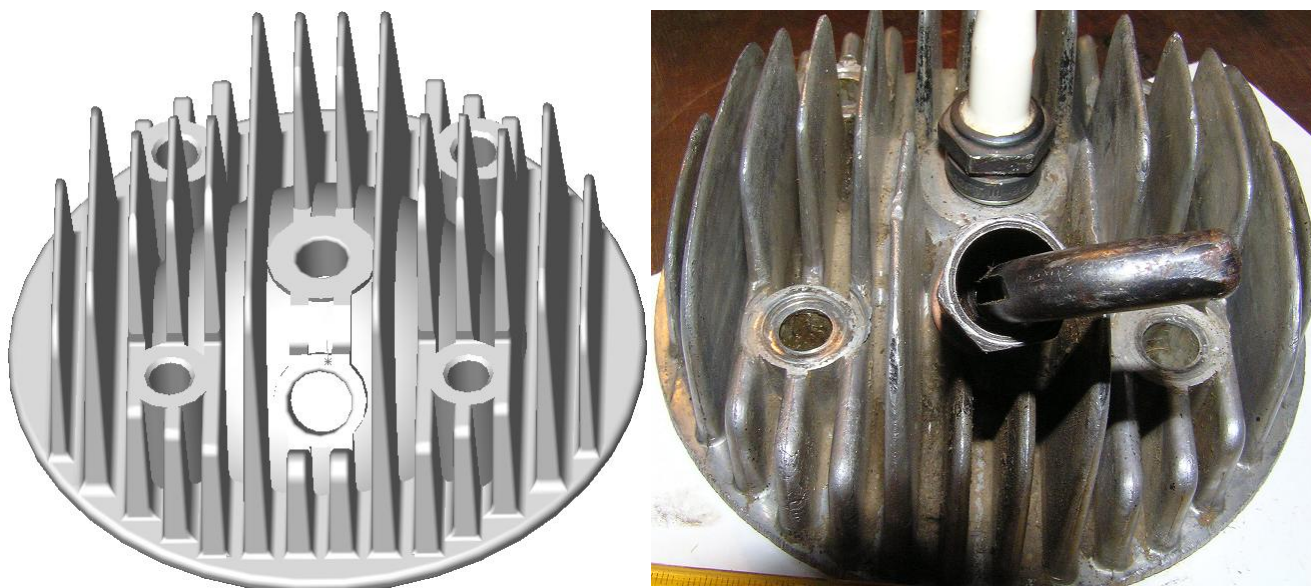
3D-модель (слева) головки цилиндра (справа) двигателя
